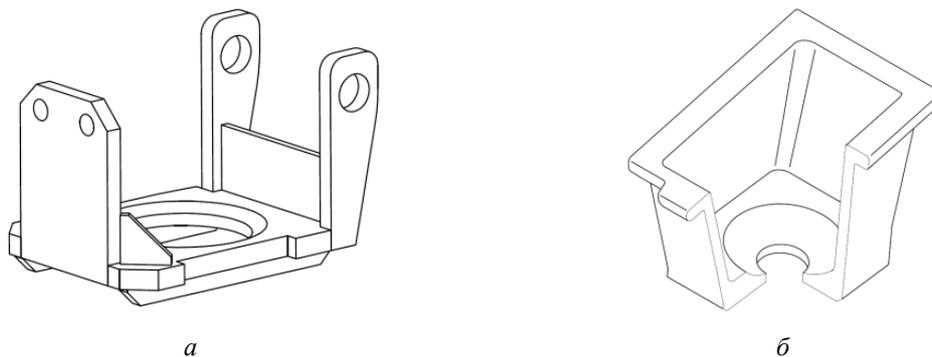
Базовые конструкции сварного (а) и литого (б) вкладыша
